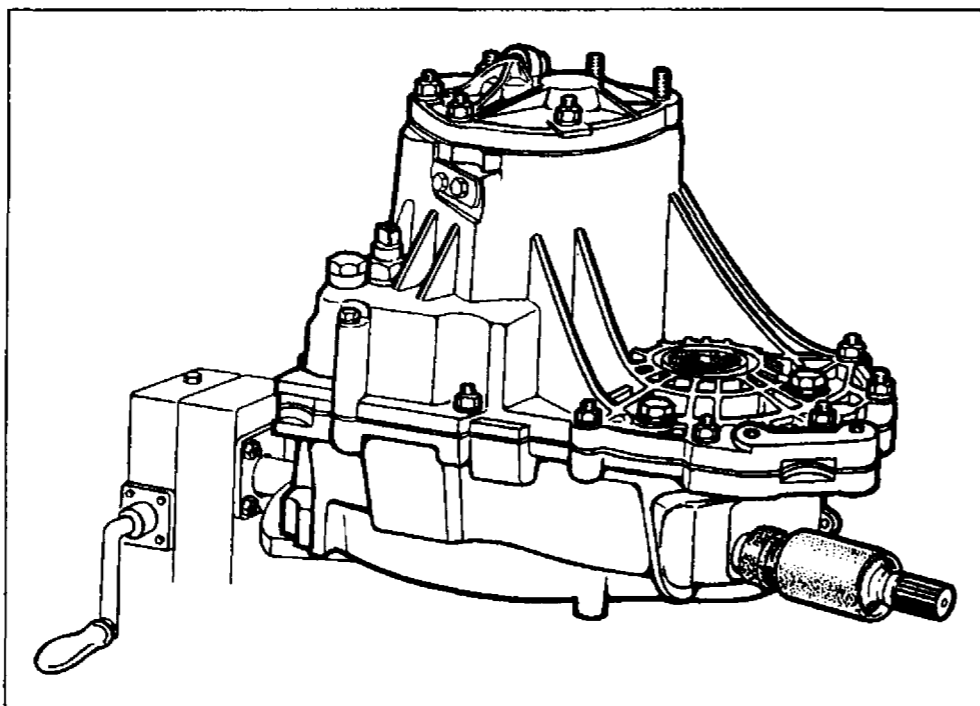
Коробка передач, установленная на стенде для разборки и сборки
